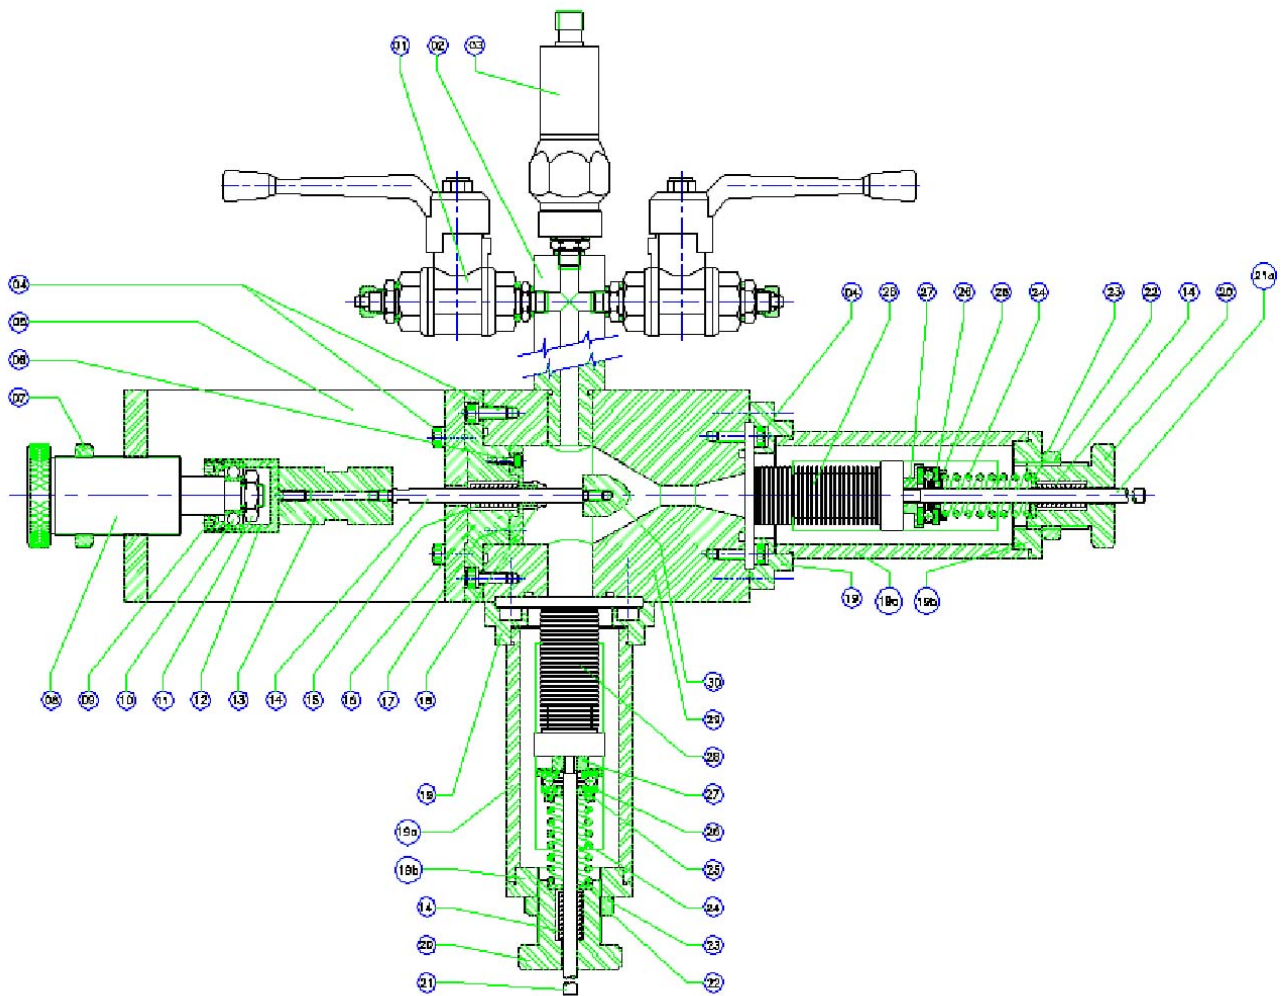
Desenho de conjunto em corte do amortecedor ativo.
